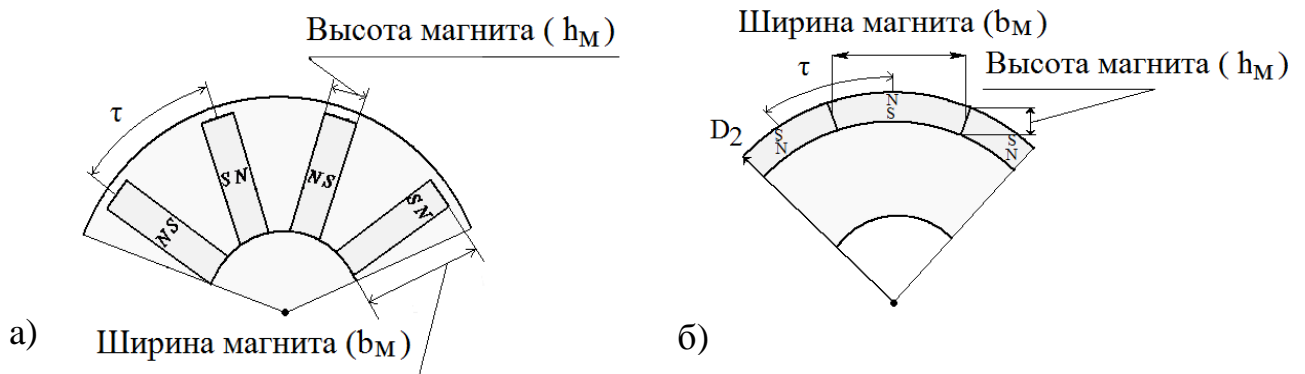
Условные обозначения размеров магнитов ротора: а – ротор коллекторного типа; б – ротор с рад. магнитами;
